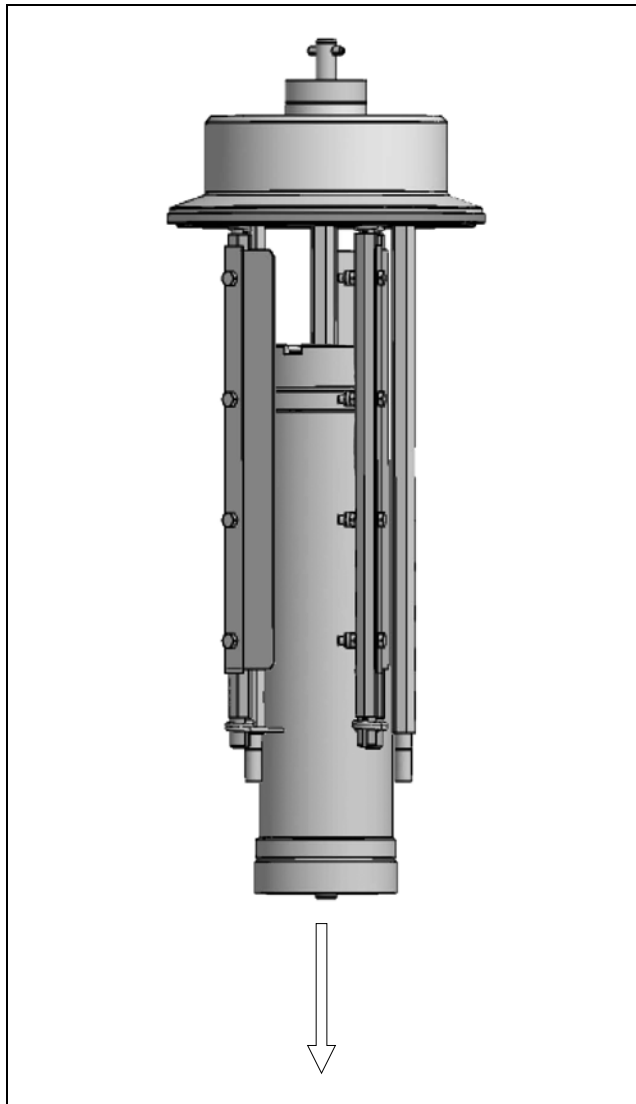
Démontage de l'ensemble de la bobine de filtre
